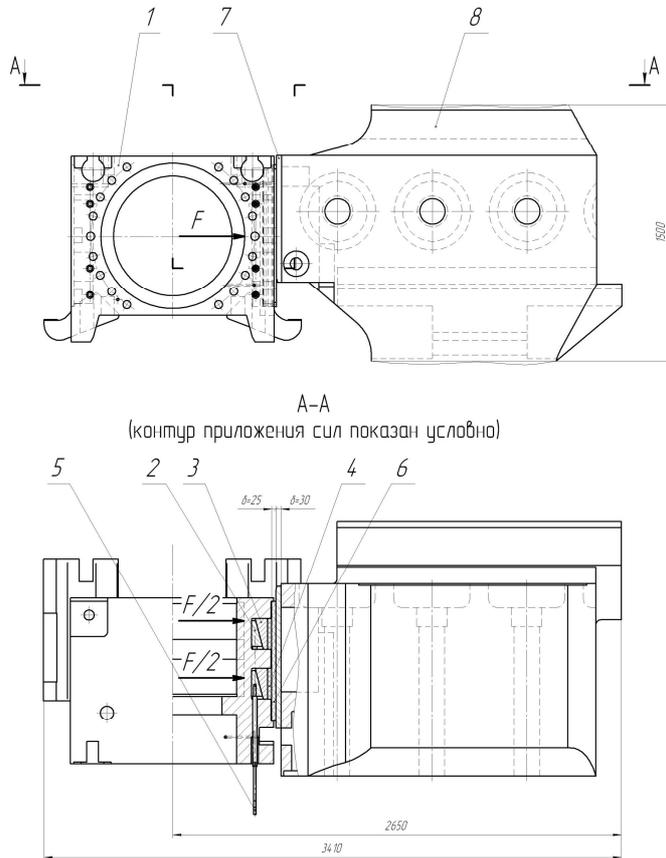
Схема навантаження ММ силою F : 1 – подушка НРВ; 2 – клин приводної; 3 – клин подвижний; 4 – вставка; 5 – рычаг; 6 – наделка подушки НРВ; 7 – лицева планка; 8 – станина
